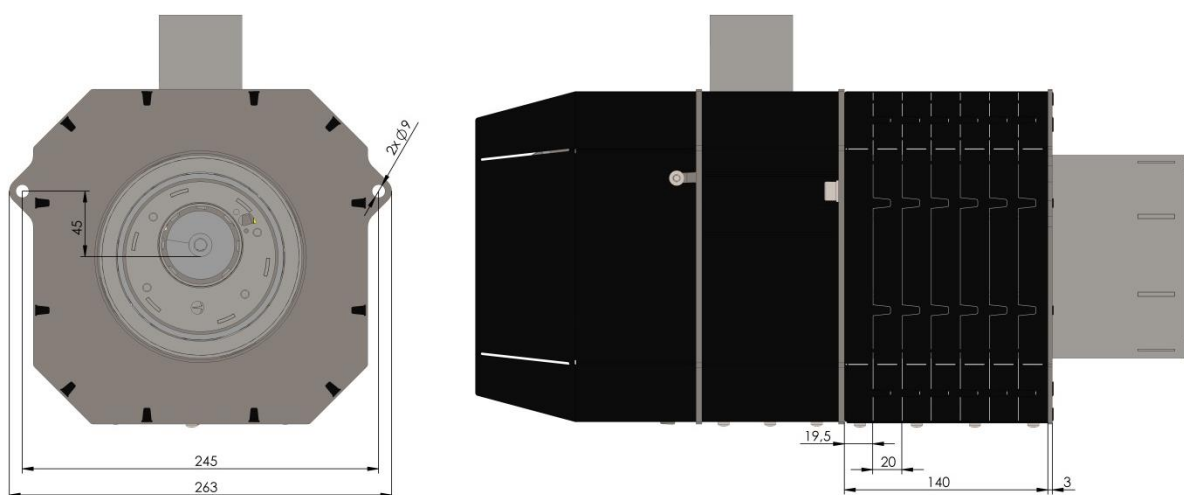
Zobrazení hořáku 6-26 kW s izolačním pláštěm a montážní přírubou
